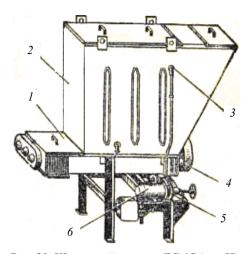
Шнековый дозатор ДС-15 (тип II): I — винтовые конвейеры; 2 — бункер; 3 — датчик уровня; 4 — привод винтовых конвейеров; 5 — клиноремённый вариатор; 6 — электродвигатель (мотор-редуктор)
